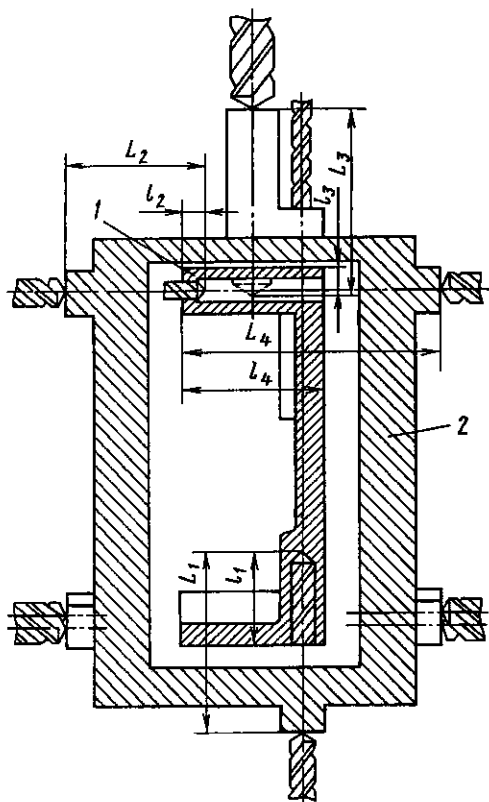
Схема наладки инструментов многошпиндельного сверлильного станка с помощью шаблона:
